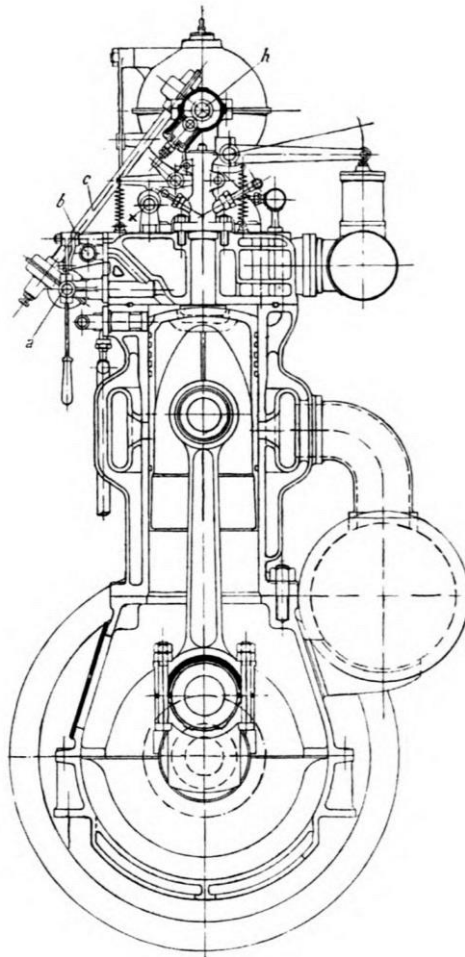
300-сильний реверсивний нафтовий двотактний шестициліндровий судовий двигун внутрішнього згоряння конструкції Луцького
